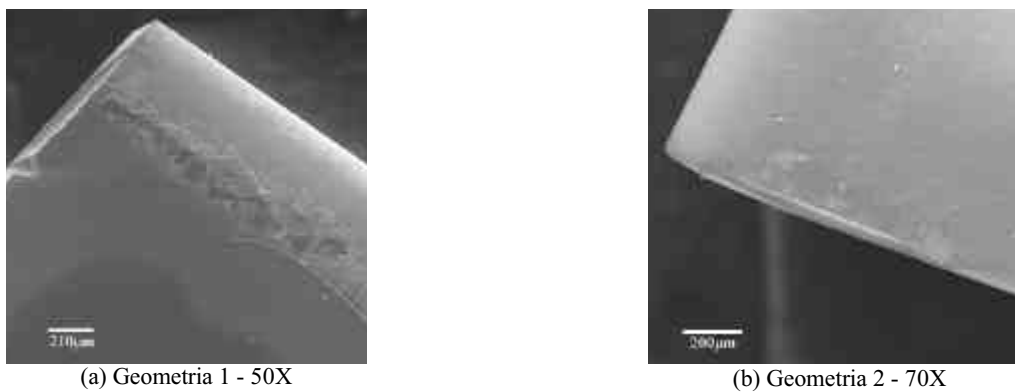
Condição de desgaste da ferramenta de PCBN após 22 segundos.
